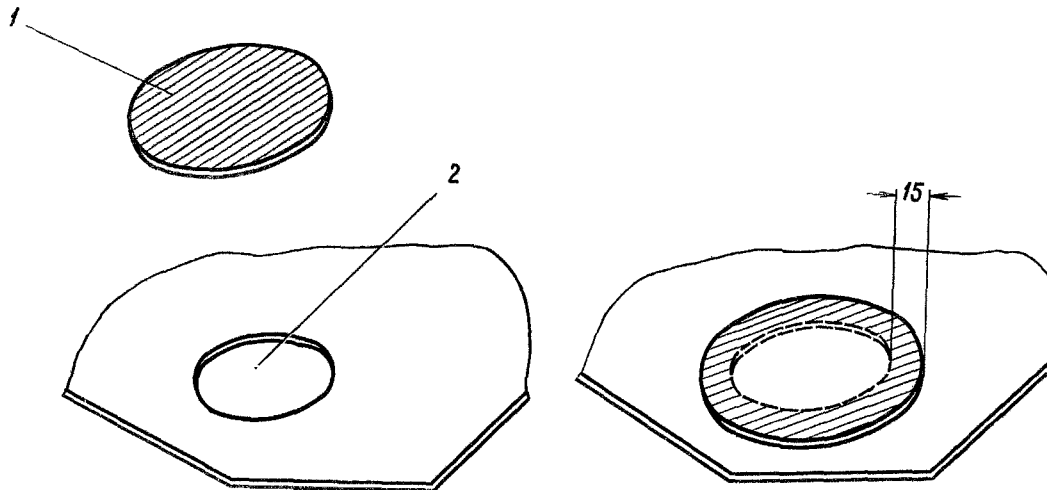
Типовой ремонт пробоин на обшивке хвостовых отсеков лопасти несущего винта:
